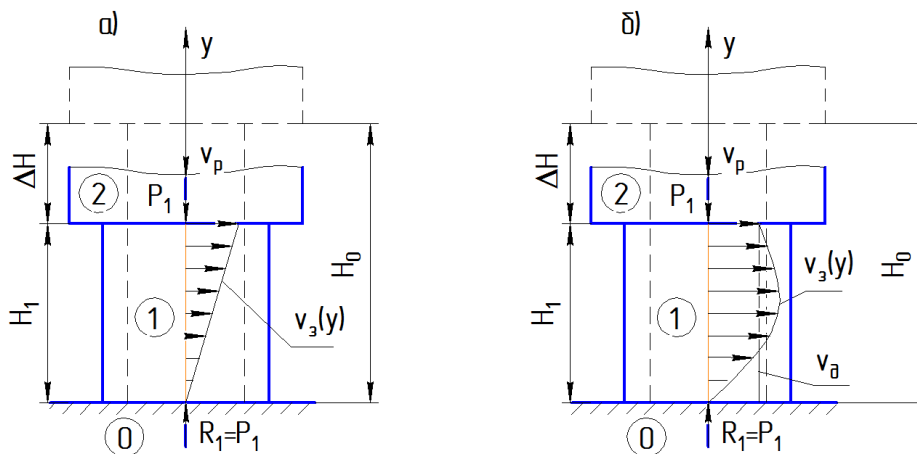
Схемы распределения скорости деформации заготовки по высоте заготовки при осадке: а – линейный закон, б – нелинейный закон
